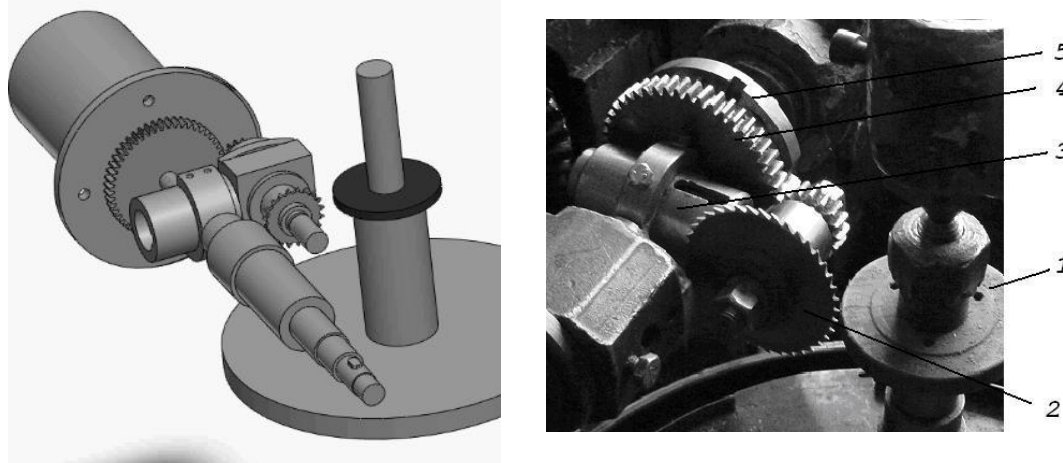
3D модель і мультиплікатор зубофрезерного верстата
